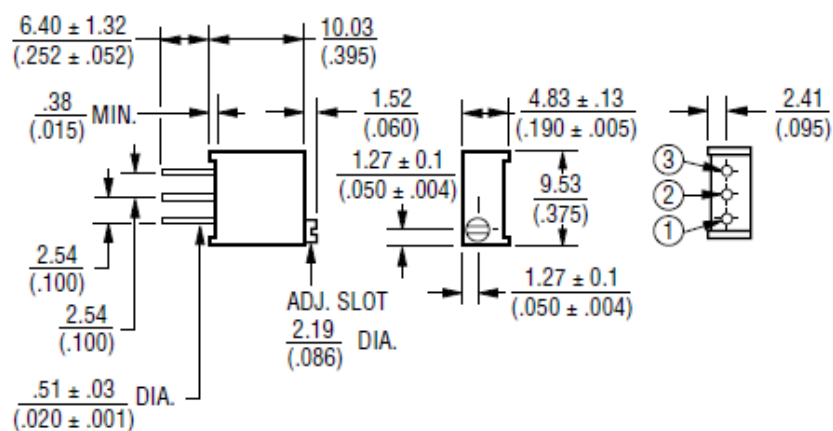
Зовнішній вигляд та габаритні розміри підстроювального резистора 3296W
